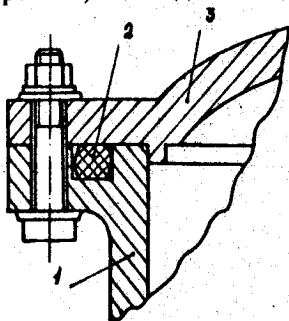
Вузол з додатковим самоущільненням фланцевого з'єднання герметизованого корпусу: 1 – корпус; 2 – герметизуюча прокладка; 3 – фланець
